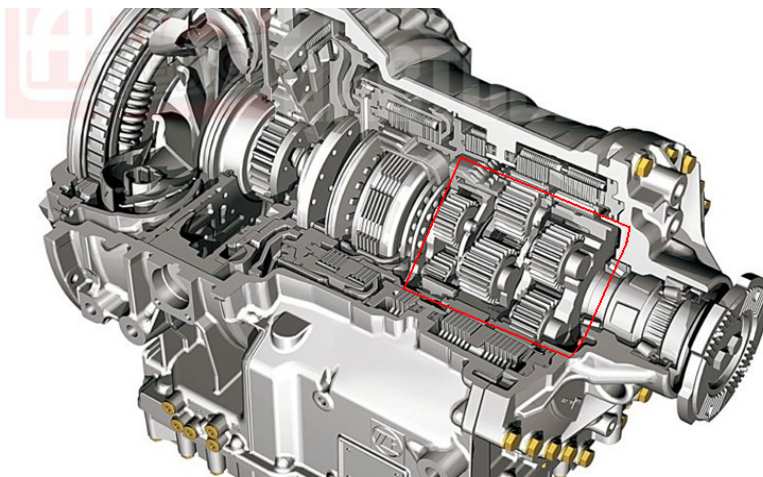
Разрез автоматической коробки передач с планетарным редуктором
